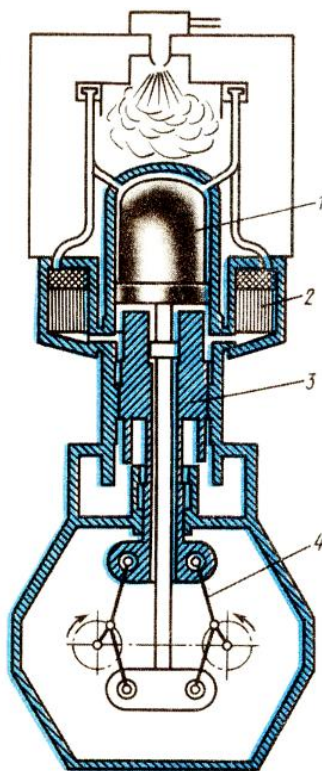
Схема двигателя Стирлинга: 1 – вытеснитель; 2 – регенератор; 3 – поршень; 4 – ромбический механизм
